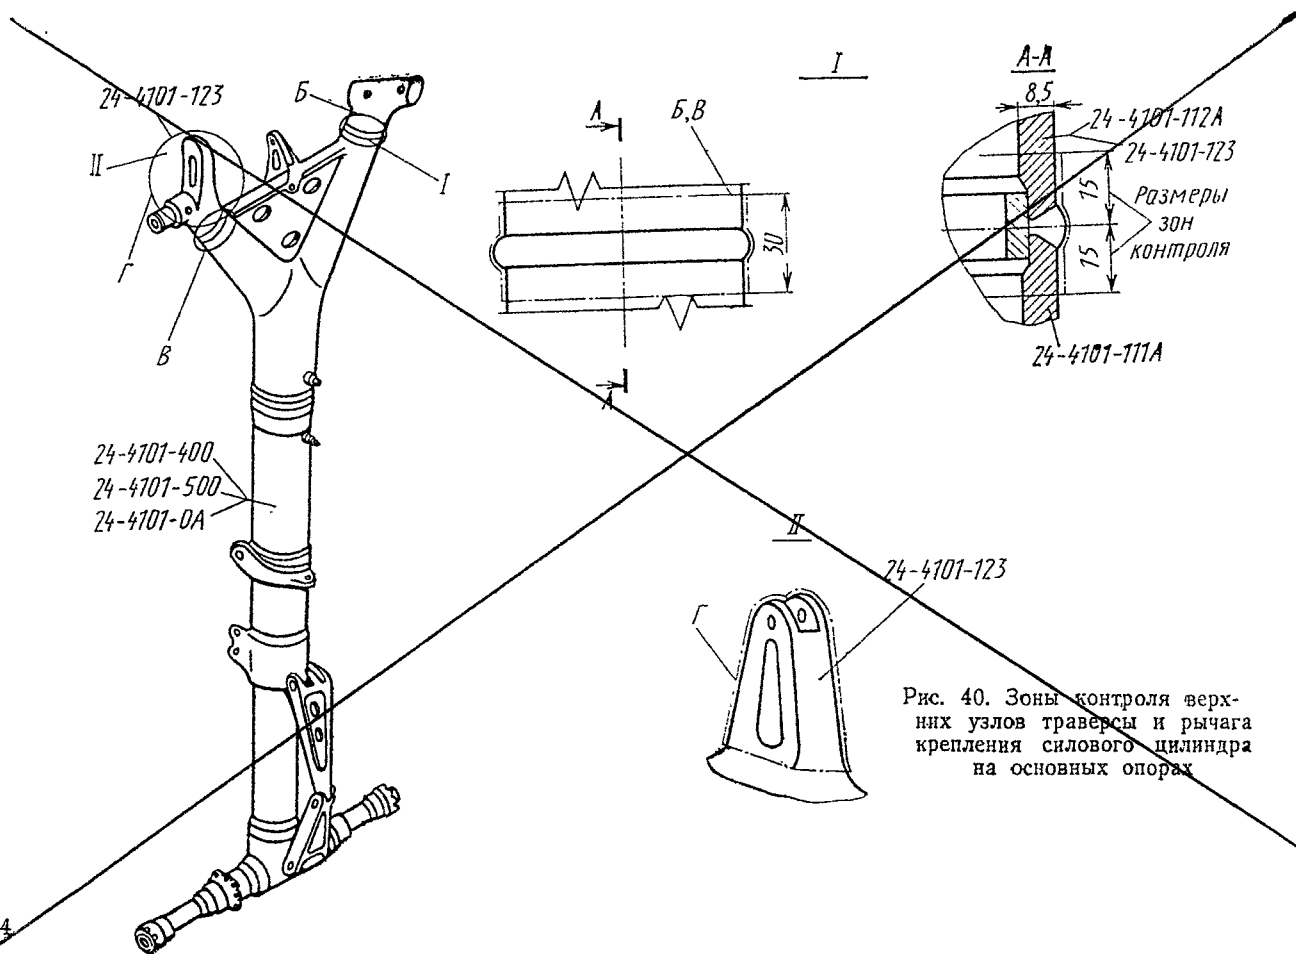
Зоны контроля верхних узлов траверсы и рычага крепления силового цилиндра на основных опорах
